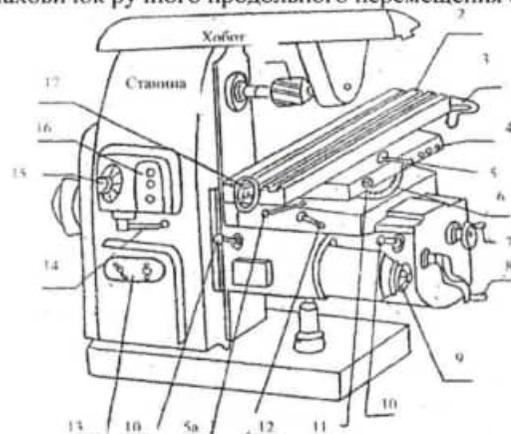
Общий вид универсального горизонтально-фрезерного станка
